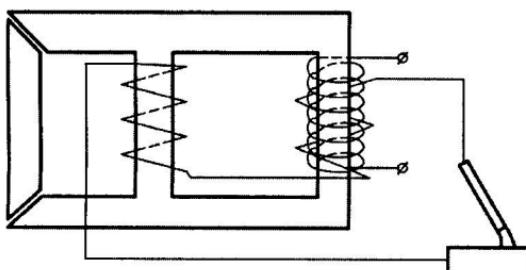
Зварювальний трансформатор Нікітіна
